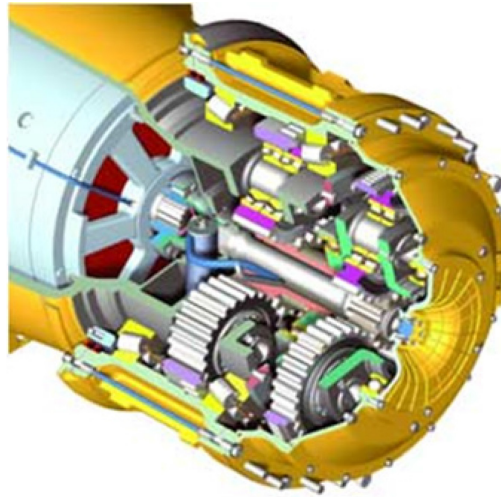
Редуктор мотор-колеса (РМК) самосвала
